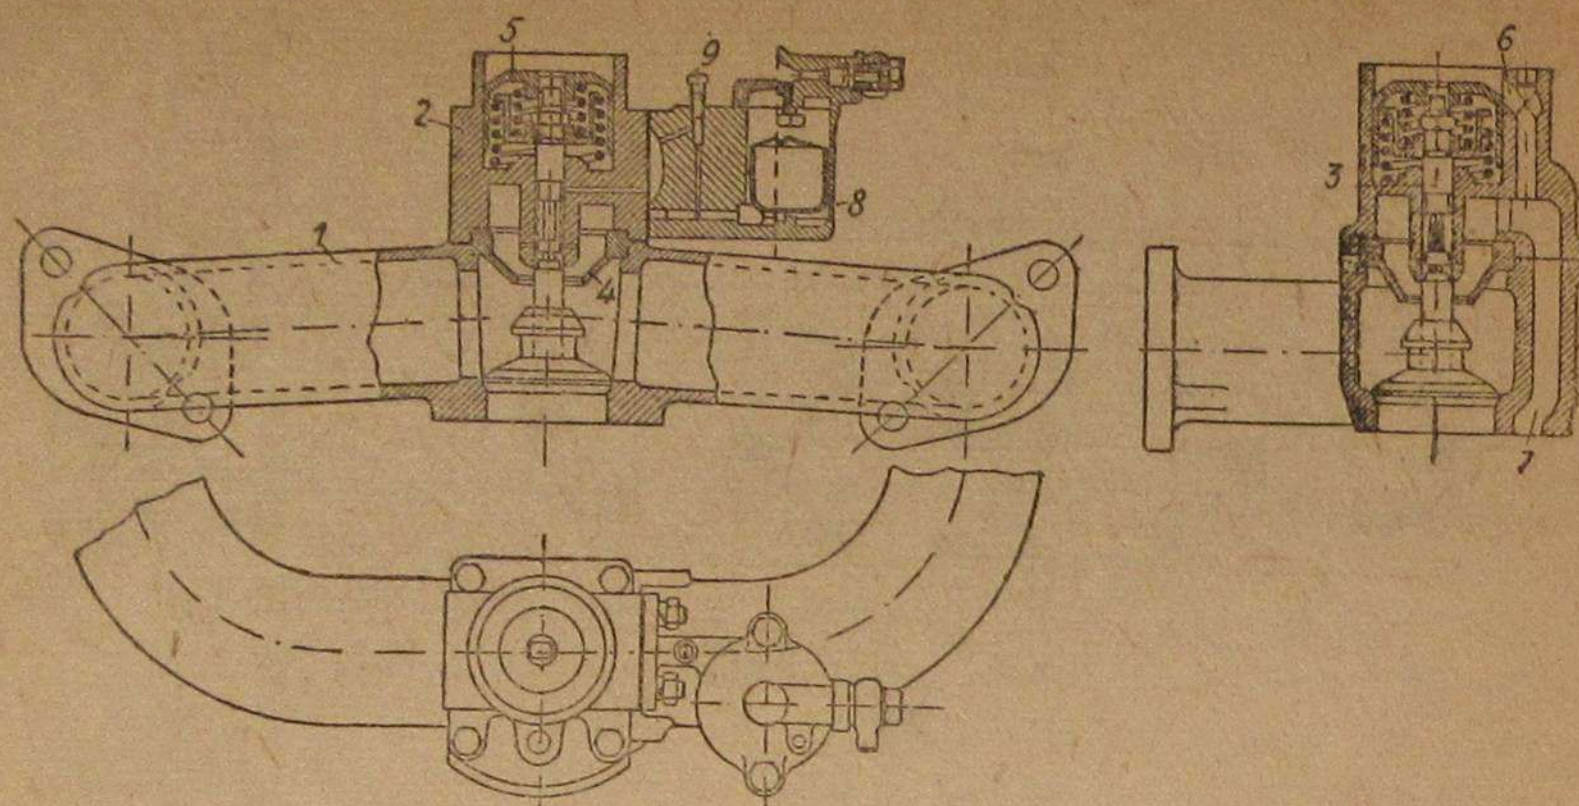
ОБЩИЙ ВИД ПУСКОВОГО КАРБЮРАТОРА И ЗАПОРНОГО КЛАПАНА:
